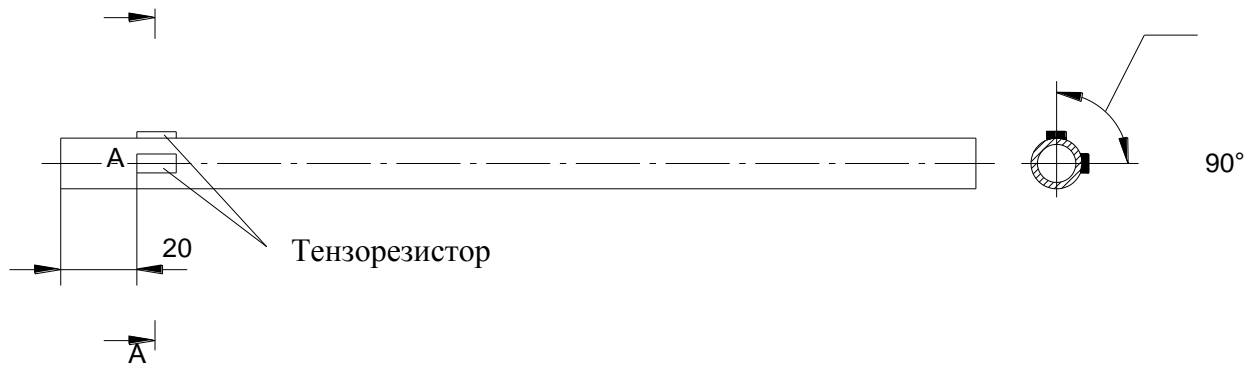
Схема и координаты наклейки тензорезисторов на образцы труб.
